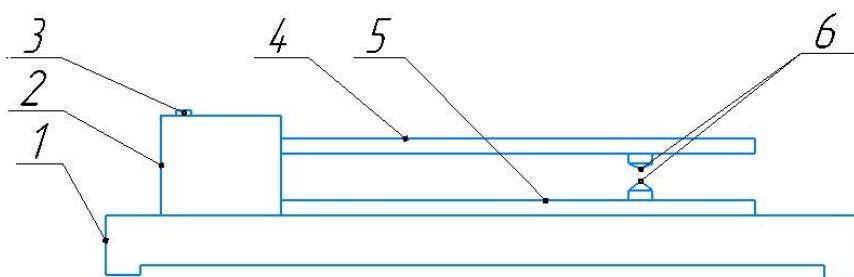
Схема учебной установки для точечной контактной сварки различных металлических изделий
